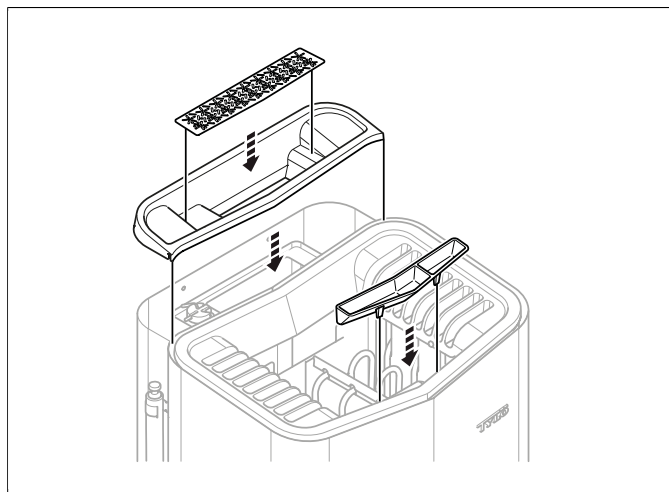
Установка крышки на бак воды, сита для трав, подставка для флакона с ароматизатором/увлажнителя воздуха
